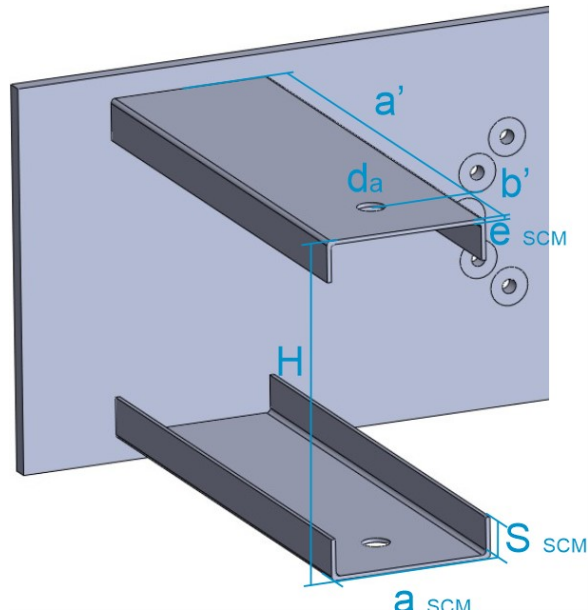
Dimensiones del soporte del conjunto móvil.
